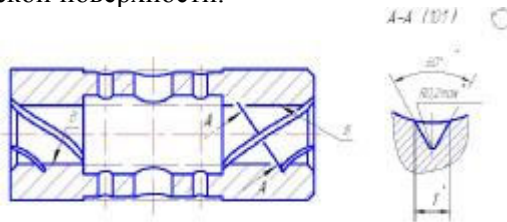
Усовершенствованный подшипник турбокомпрессора ТКР-6,5.1
